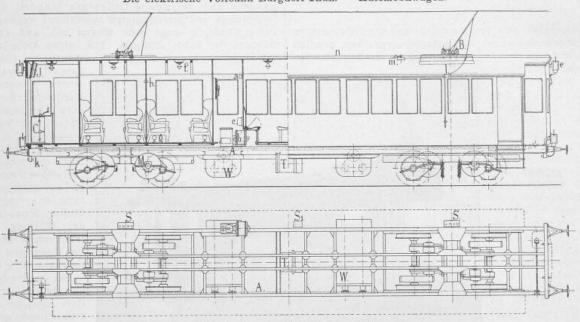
Ansicht und Grundriss. 1:100,
